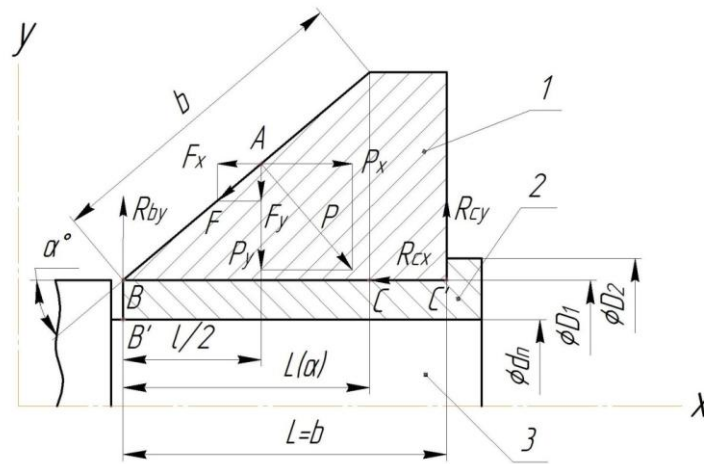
Схема действие сил на коническом формующем элементе и реакции опор на подшипнике: 1 – конический элемент; 2 – подшипник; 3 – вал вала
